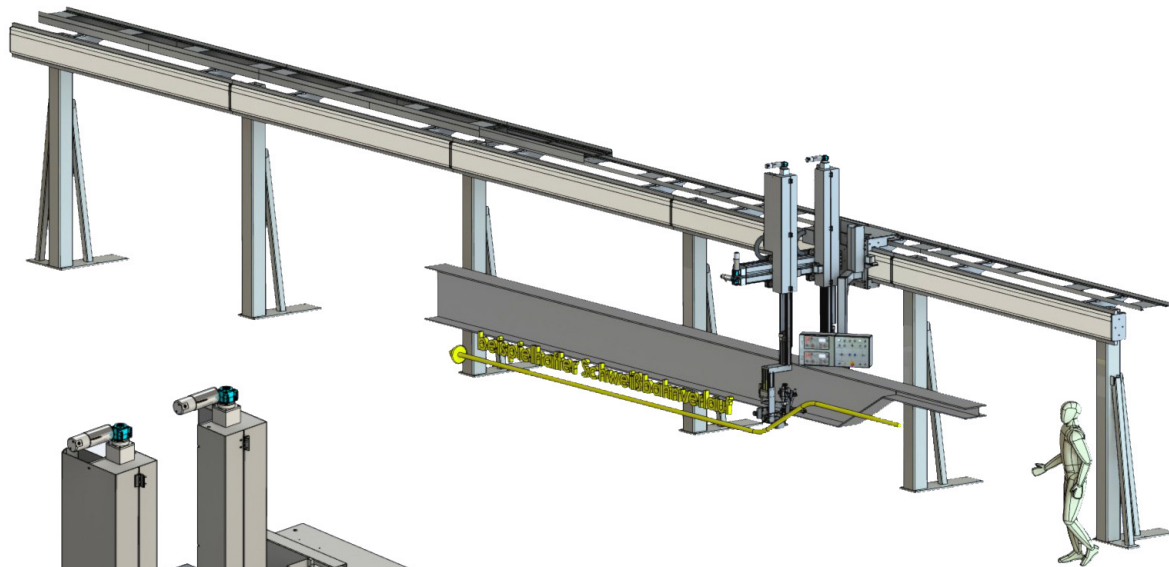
Trägerschweißvorrichtung 20 m
